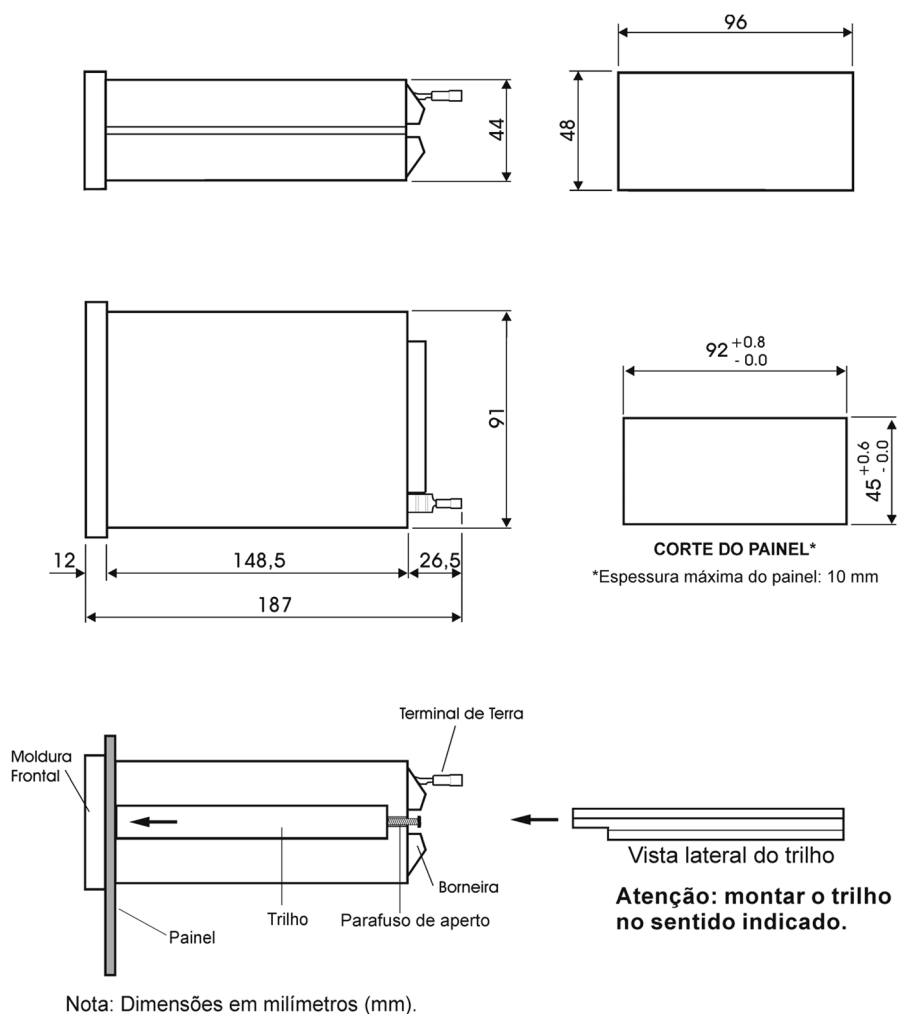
Desenho dimensional, corte e vista lateral da montagem no painel
